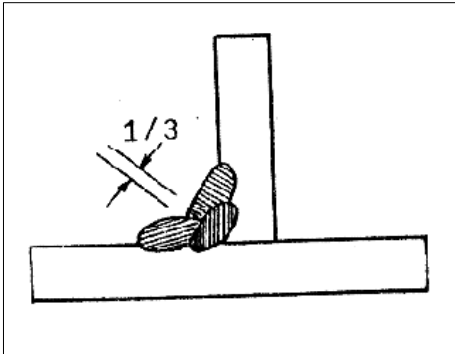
Pasos para soldadura en ángulo interior
